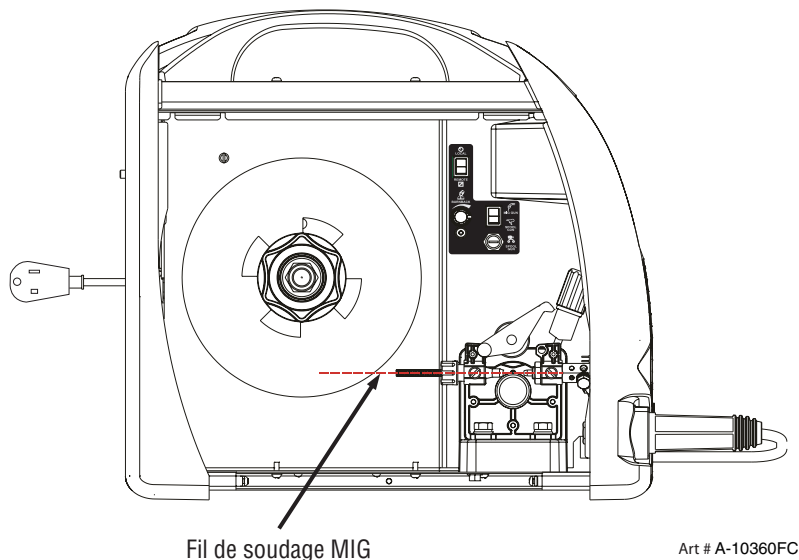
Fil de soudage MIG - Pose
